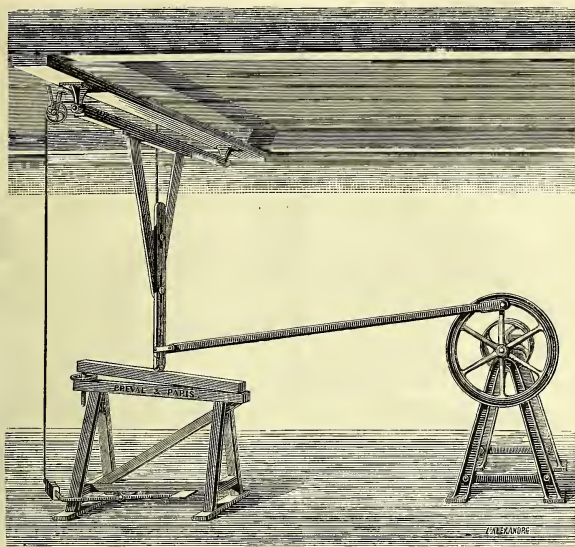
Machine à *ébutter* et à lisser le maroquin.
